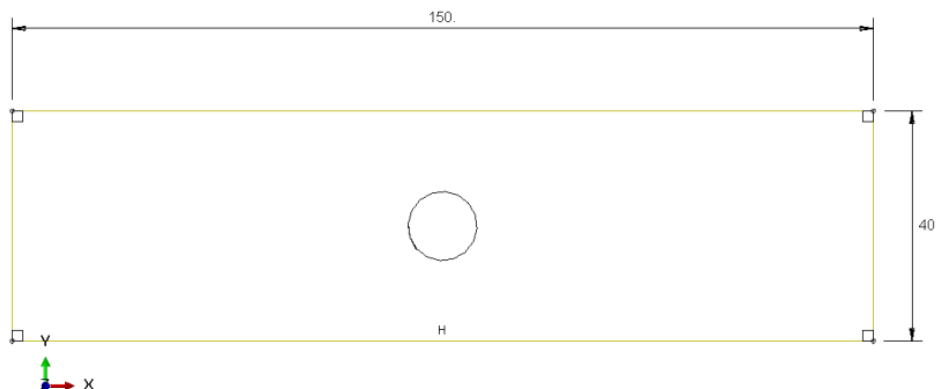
Dimensiones exteriores de las probetas de ensayo.
